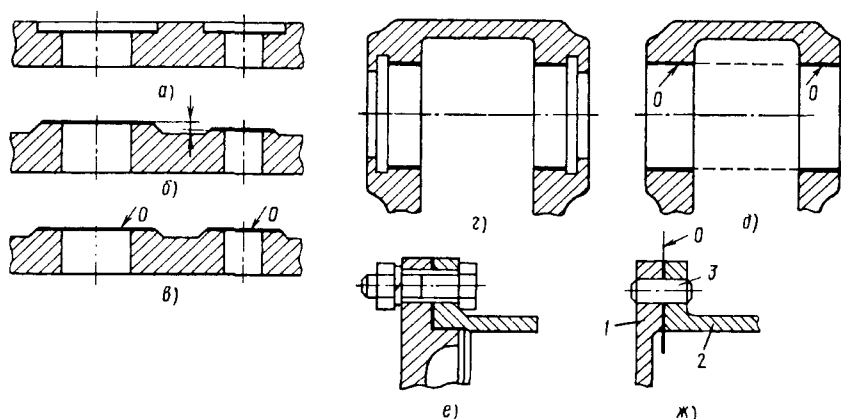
Примеры изготовления поверхностей деталей напроход
